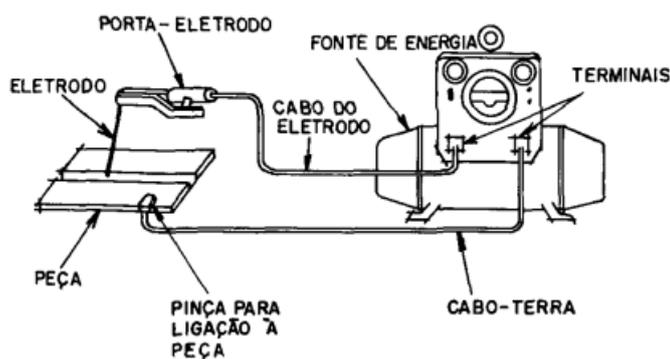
Equipamentos utilizados para soldagem com eletrodo revestido
